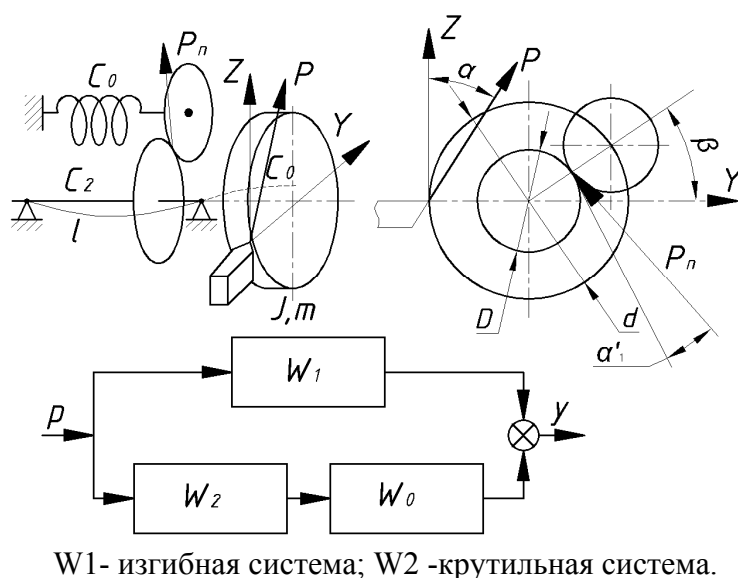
Расчетная схема УС шпиндельной группы токарного станка
